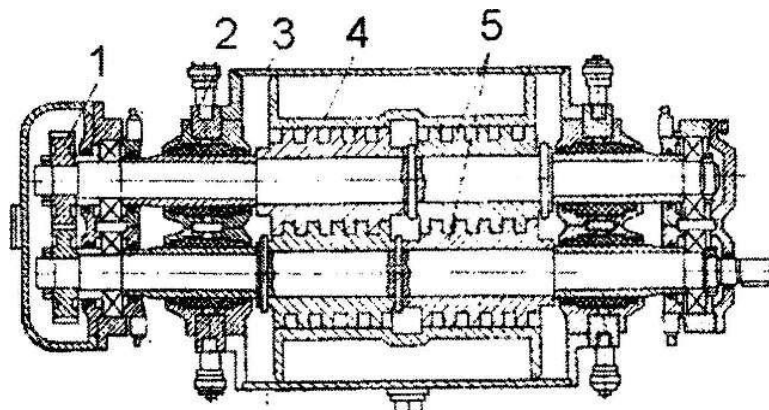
Двухвинтовой насос типа 2BV 1 - синхронизирующие шестерни; 2 - уплотнение; 3 - корпус; 4 - обойма; 5 - ведущий и ведомый винты (роторы)
